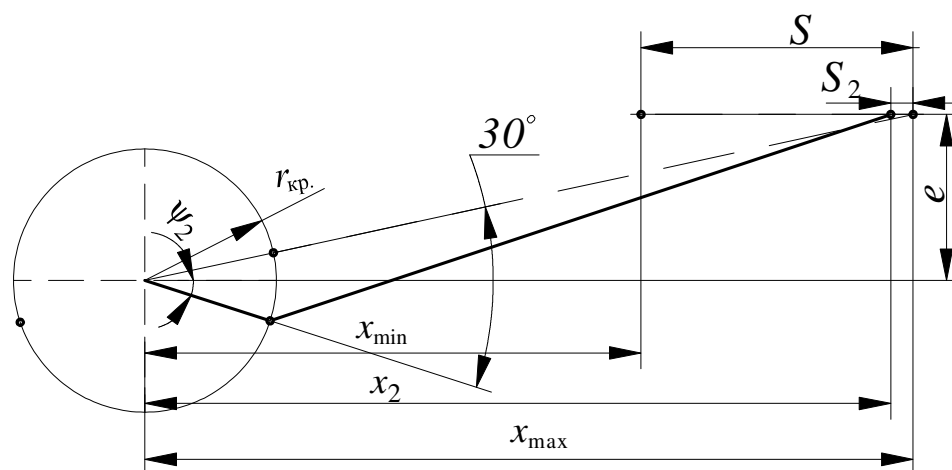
Схема движения клетки при повороте заготовки
